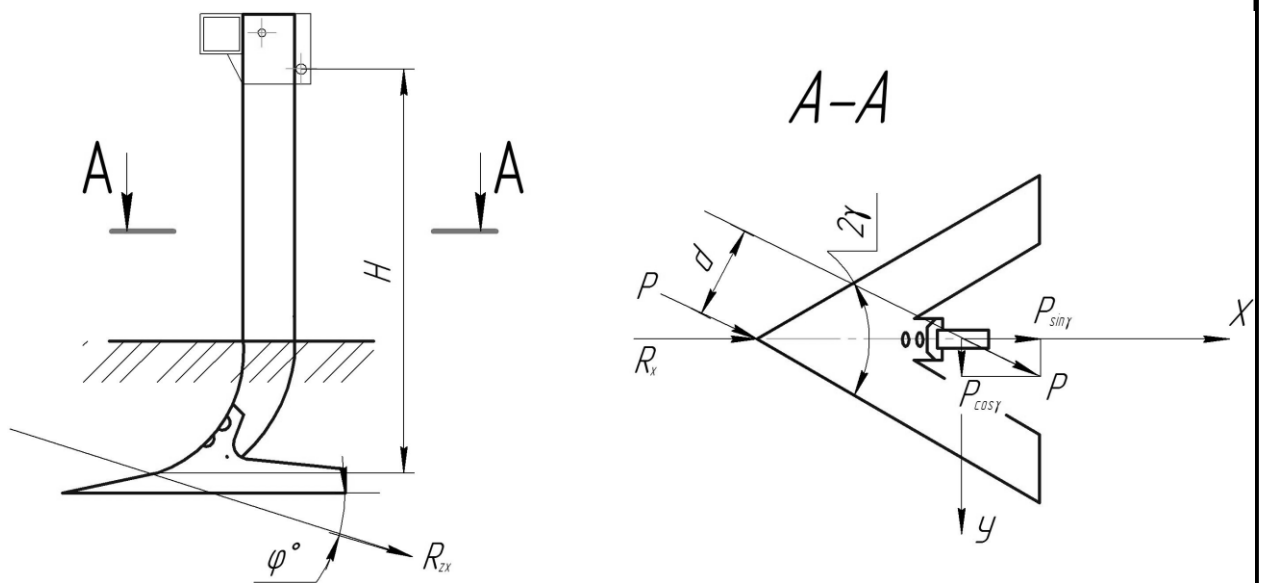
Розрахункова схема для стійки культиваторної лапи
